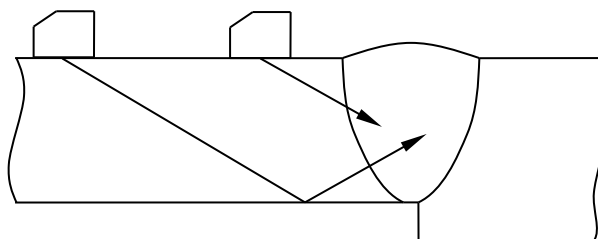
Схема контроля сварных соединений с разной толщиной свариваемых элементов
